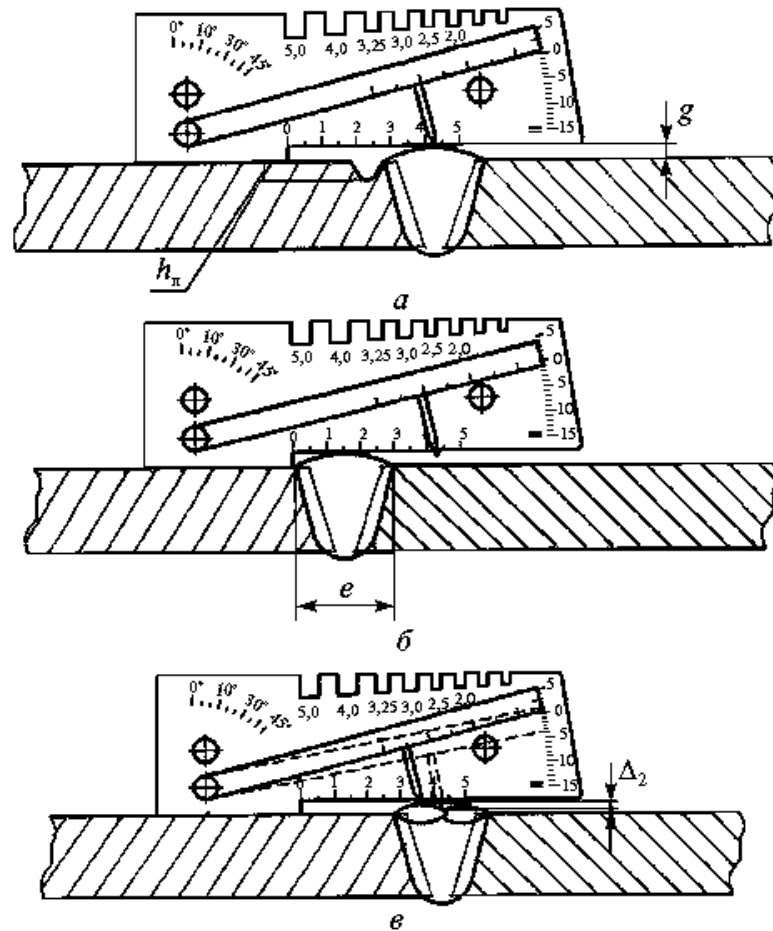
Измерения с помощью шаблона УШС размеров сварного шва
